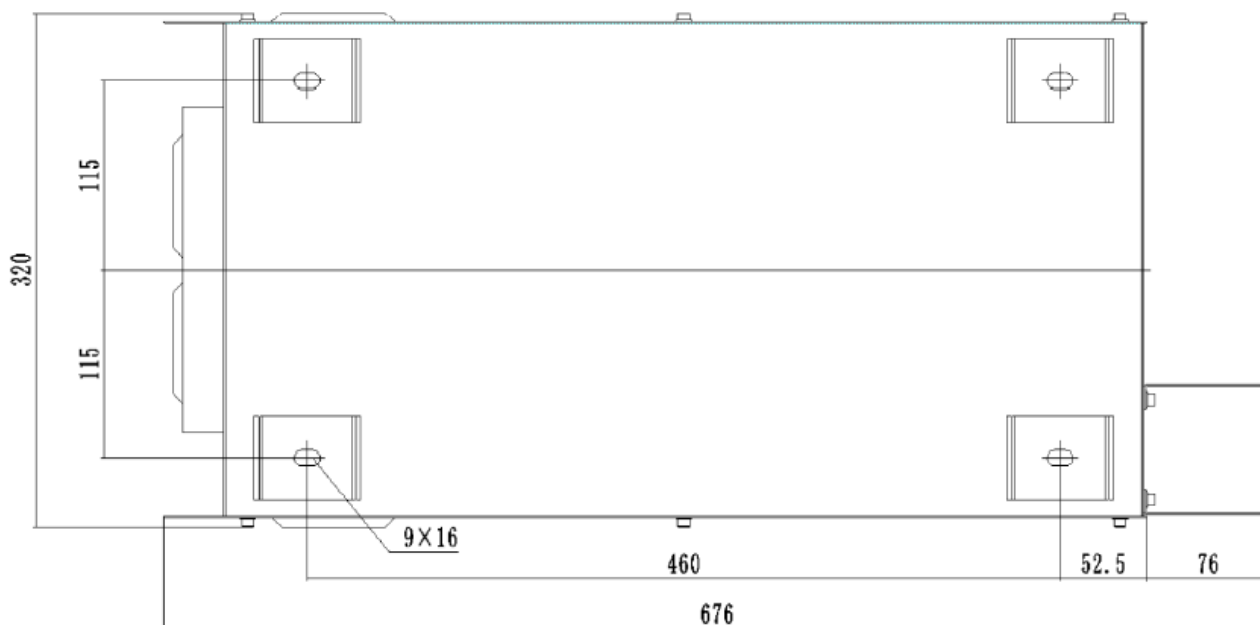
Установочные и габаритные размеры источника плазмы LGK-120HD.
